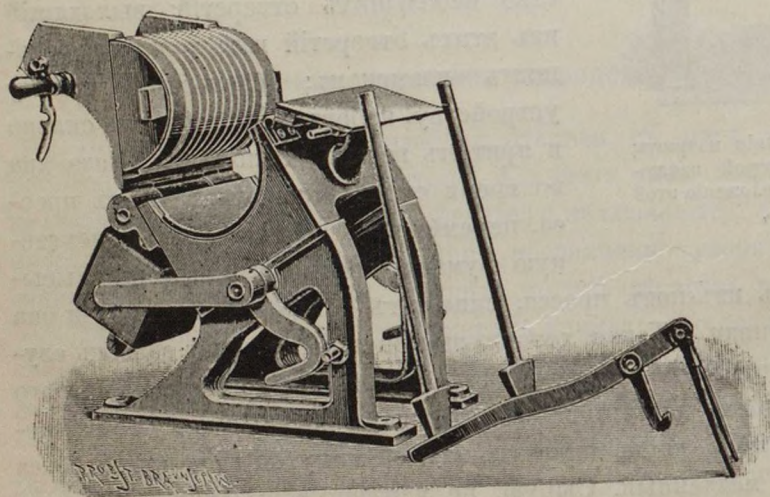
Аппаратъ для отливки стереотипа съ бумажныхъ матрицъ. Верхняя часть (полуцилиндрическая крышка) поднята — аппаратъ приготовленъ для вкладыванія матрицы.
